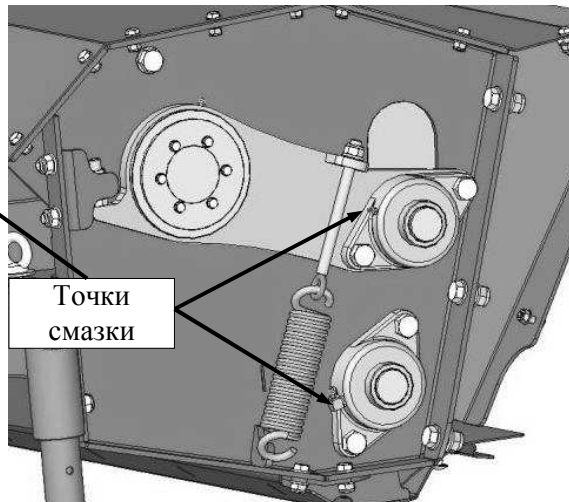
Точка смазки самоустанавливающего подшипника смазкой LT43
